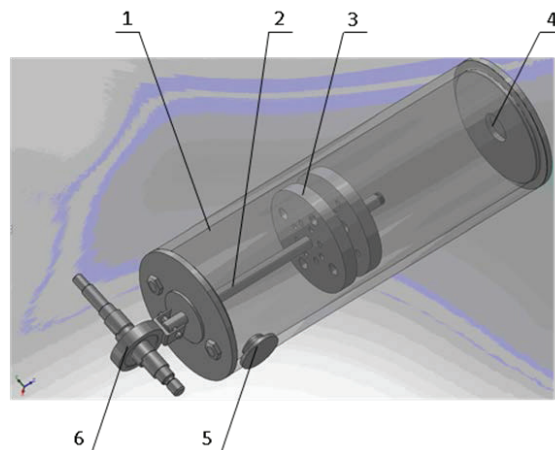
Конструктивна модель робочої камери імпульсного пристрою для гомогенізації, створена у середовищі SolidWorks: 1 – корпус у вигляді циліндра; 2 – штоковий елемент; 3 – поршні ударного типу; 4 – вхідний патрубок для подачі молока; 5 – вихідний патрубок для забору гомогенізованого продукту; 6 – кривошипно-шатунний механізм
